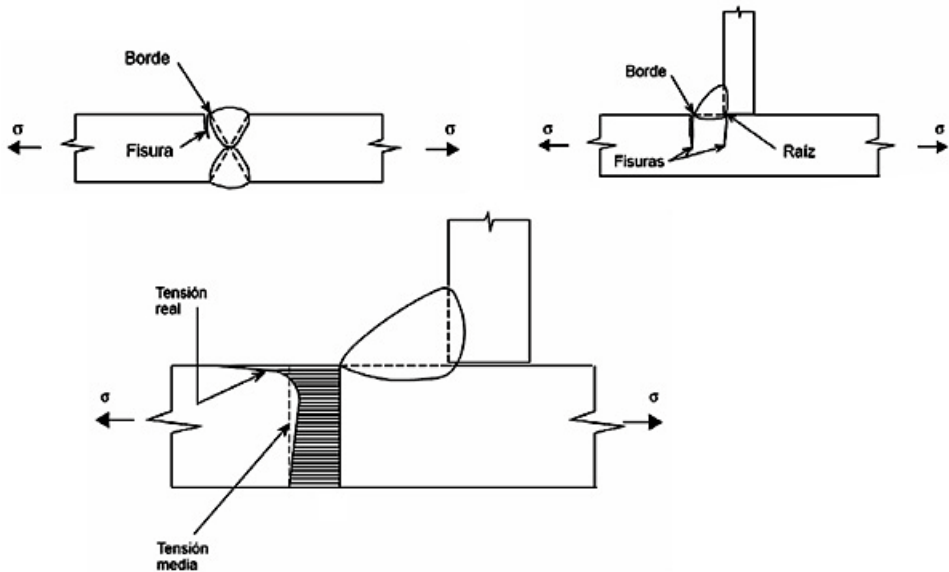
Distribución de tensiones en las chapas por efecto de las soldaduras.
